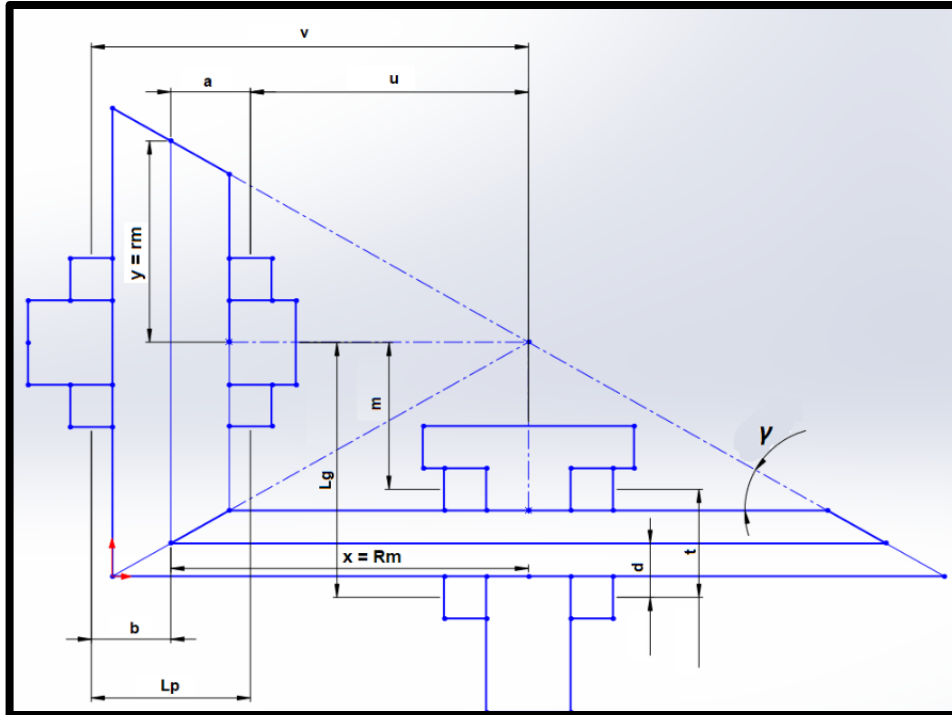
Dimensiones importantes en el dimensionamiento de los engranajes cónicos. Fuente: Propia.
